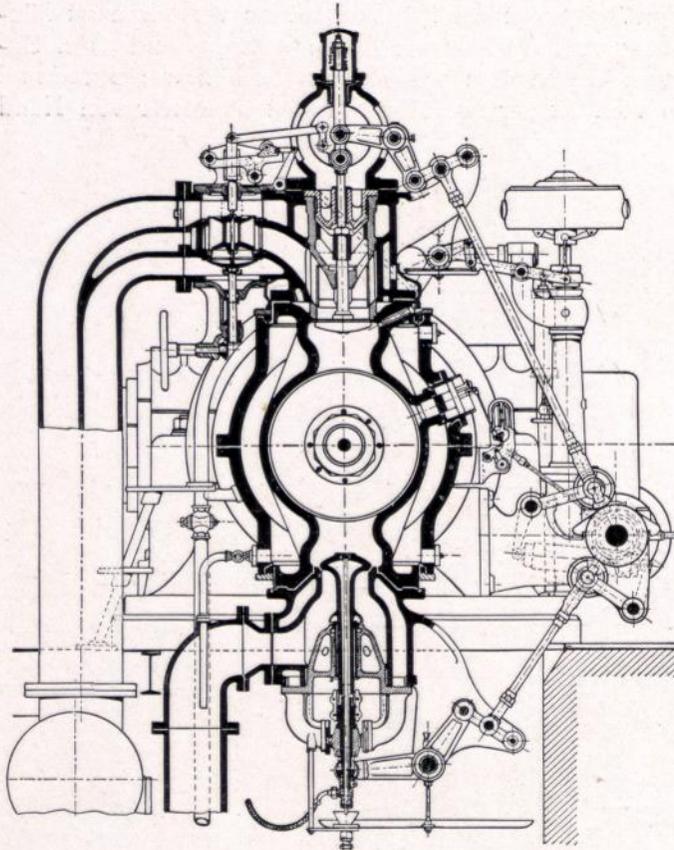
Steuerung der Deutzer Maschinenfabrik.
